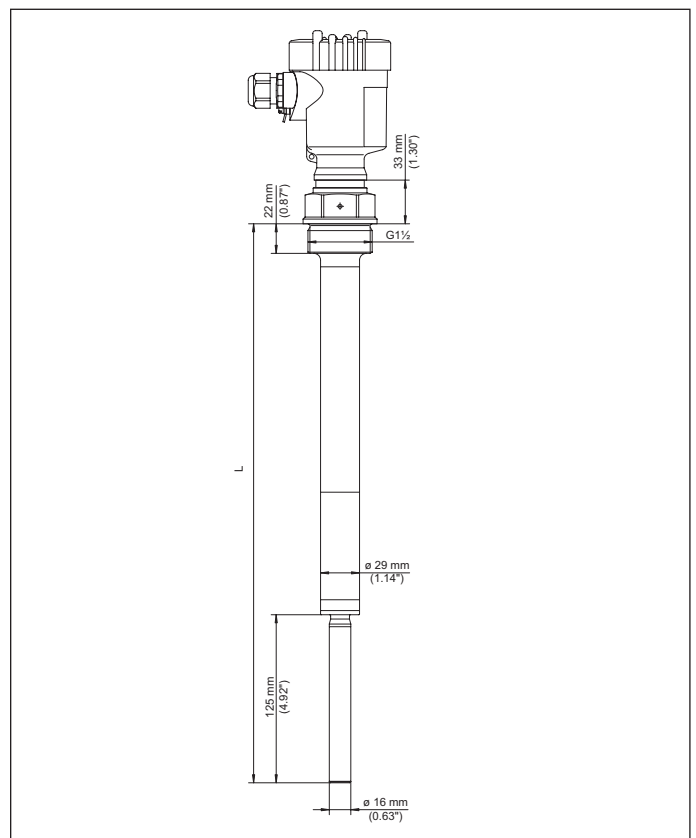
VEGAVIB 63 - Gewindeausführung G1 1/2
